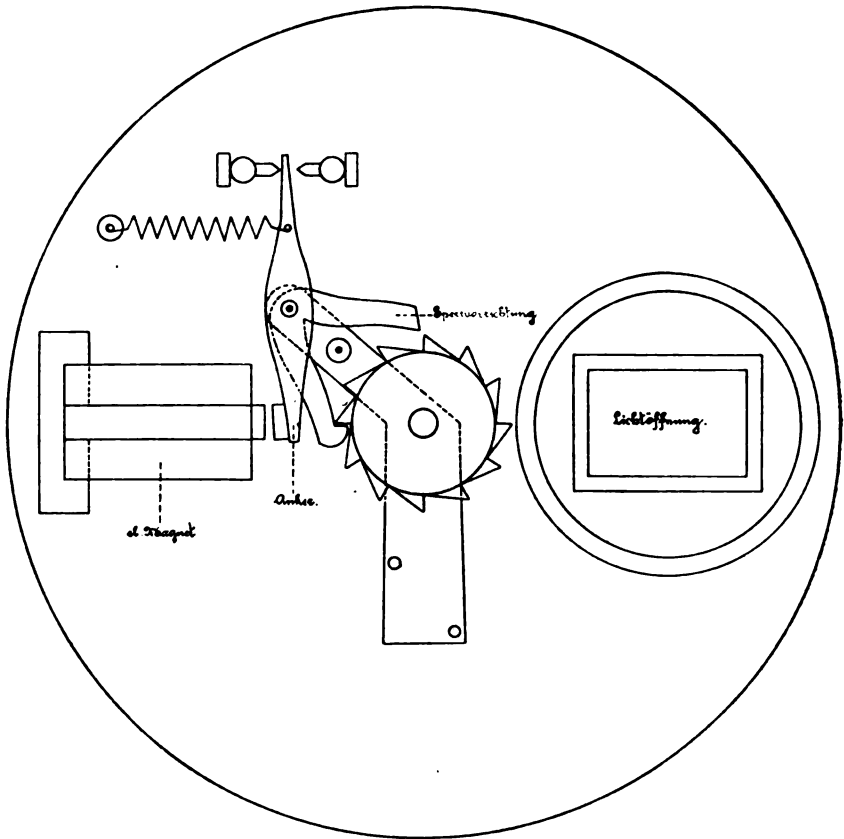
Grundriß des großen Wasserlichtmeßapparates
